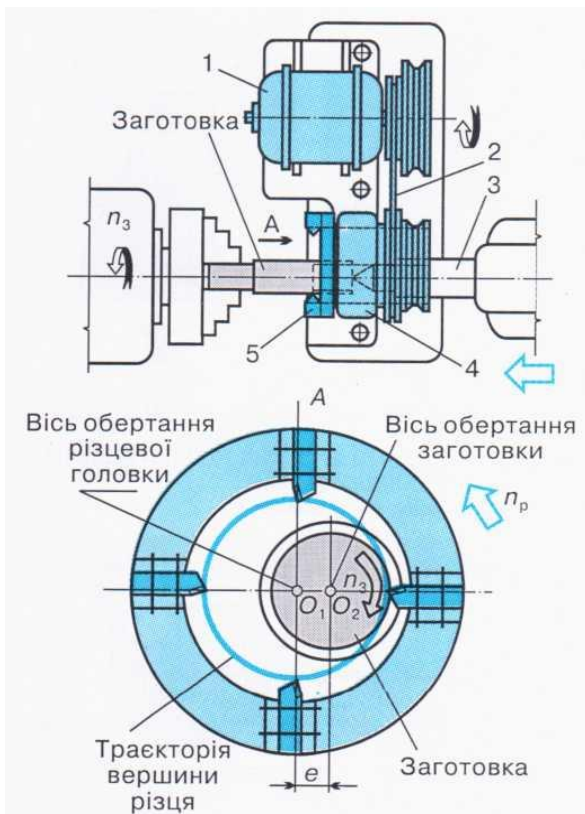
ПРИСТРІЙ ГУРГАЛЯ ДЛЯ ШВИДКІСНОГО НАРІЗУВАННЯ РІЗЬБИ:
